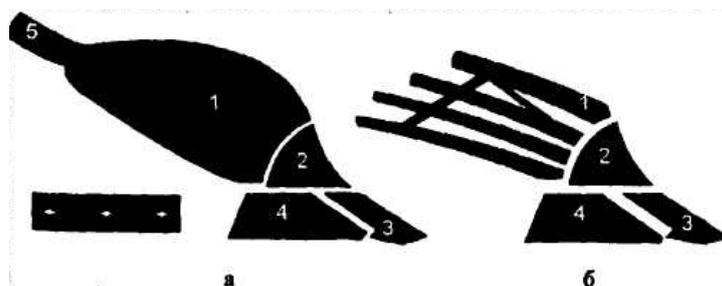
Корпуса фирмы «Эберхарт»: а - со сплошным отвалом; б - с полосовым отвалом; 1 - отвал; 2 - грудина; 3 - долото; 4 - лемех; 5 - удлинитель отвала
